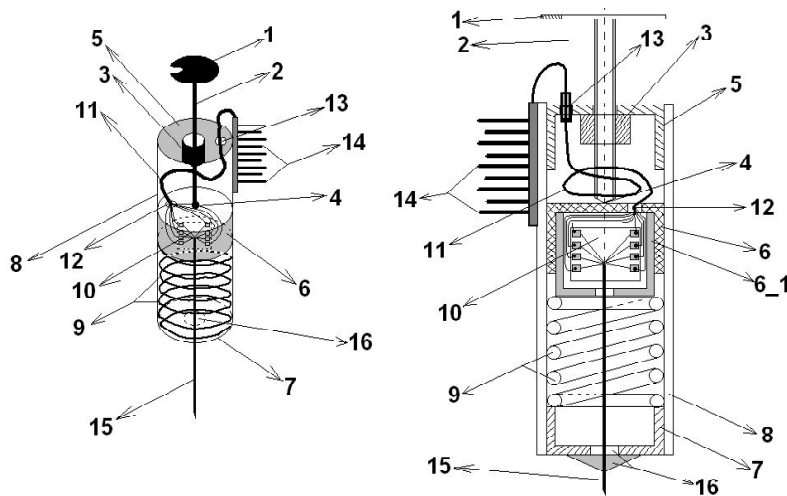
1- металевий диск з вирізкою для обертання шток-гвинта; 2- шток-гвинт з різьбою; 3- пластикова різьбова втулка; 4- упорна площадка поршня, з якою контактує конус шток-гвинта; 5- верхня циліндрична кришка мікроманіпулятора; 6- поршень мікроманіпулятора; 6_1- внутрішній герметизуючий циліндр поршня; 7- нижня циліндрична кришка поршня; 8- циліндричний корпус мікроманіпулятора; 9- пружина повернення поршня у вихідне положення; 10- сеталова контактна площадка мікроелектрода; 11- з'єднувальний гнучкий багатожильний провід (для з'єднання восьмиканального мікроелектрода з конектором); 12- герметизований отвір в поршні для контактних провідників; 13- герметизований отвір в верхній циліндричній кришці для виведення контактних провідників; 14- конектор мікроманіпулятора для з'єднання з портативним багатоканальним телеметричним підсилювачем-передавачем; 15- восьмиканальний металевий мікроелектрод; 16- силіконова герметизація вихідного отвору мікроманіпулятора для мікроелектрода.
